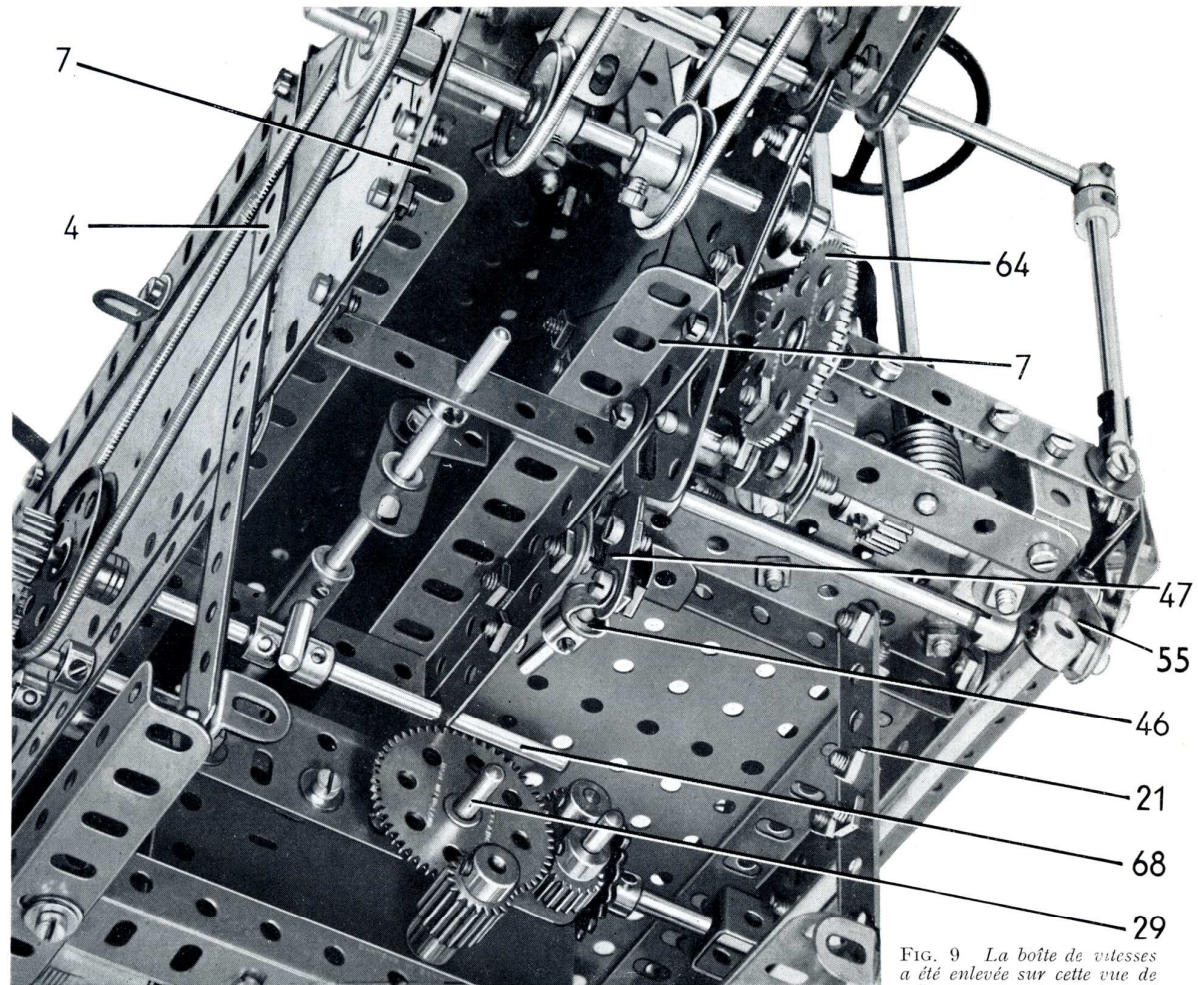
La boîte de vitesses a été enlevée sur cette vue de l'intérieur de la machine.
